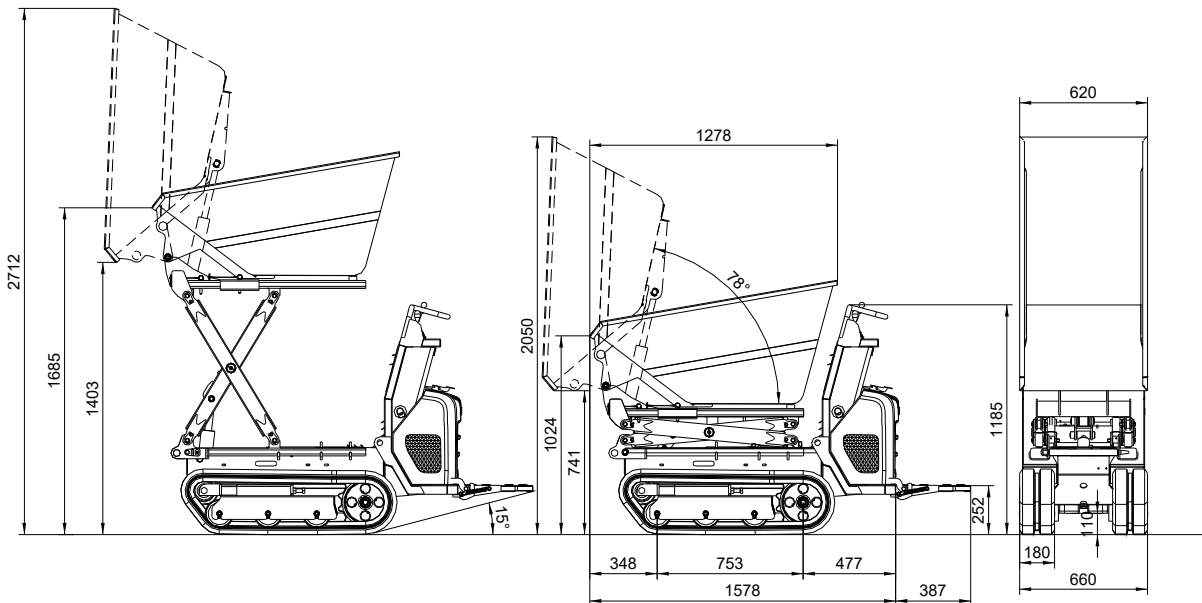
Dimensions de la machine (modèle DT05-P avec benne basculante vers le haut)
